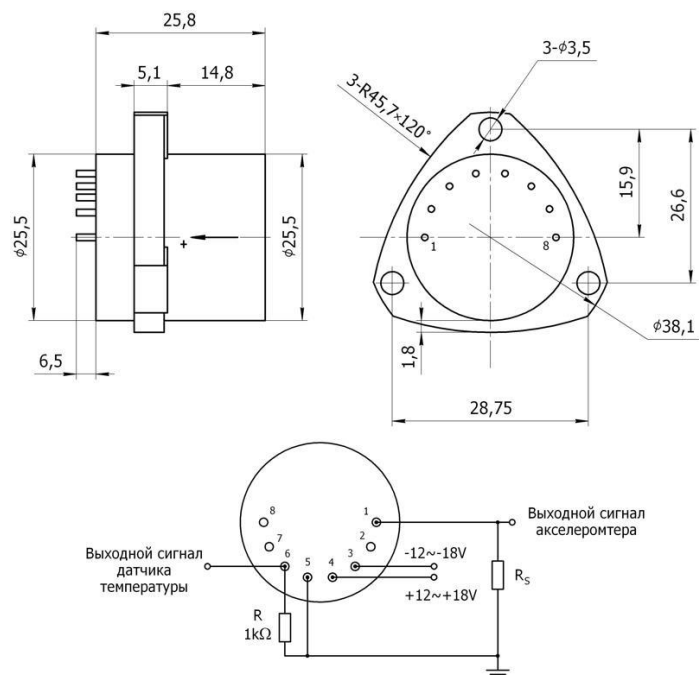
Внешний вид, габаритные размеры и схема включения *INN-202
